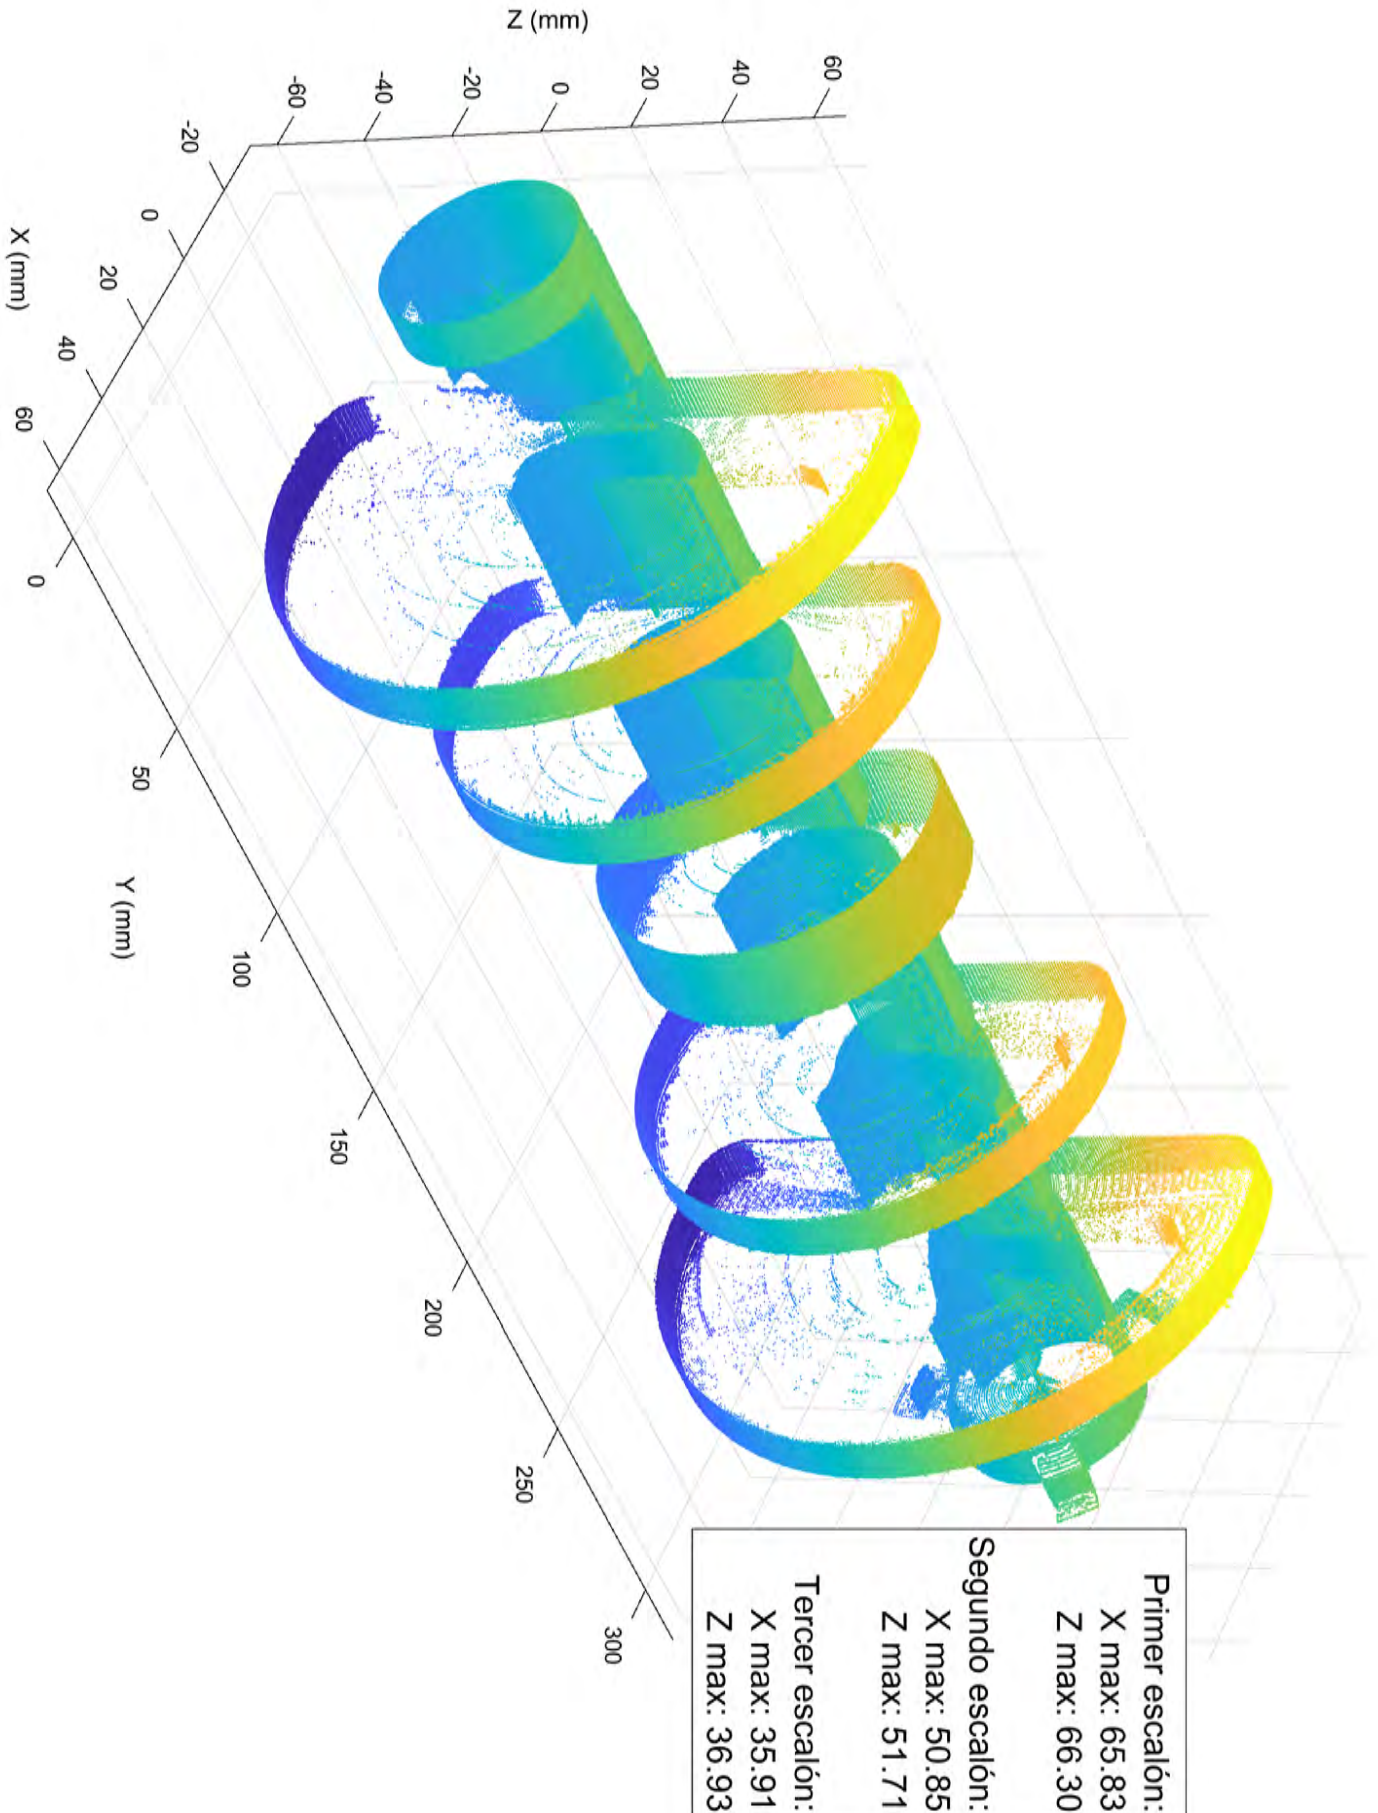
Segunda reconstrucción tridimensional del cilindro de calibración final
